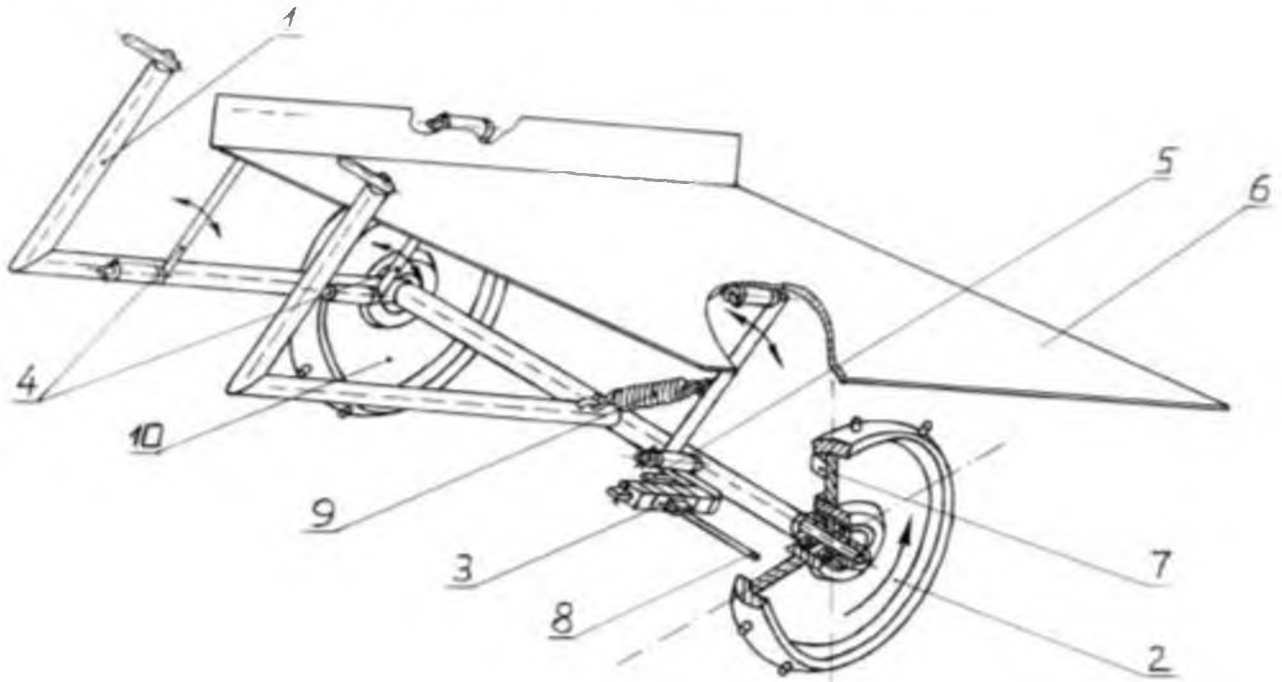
Схема удосконаленого розстиляльного пристрою стеблової стрічки льону: 1 – рама; 2 – опорно-приводне колесо; 3 – коромисло; 4 – підвіски; 5 – обмежувач ходу; 6 – вібрувальний щит ; 7 – язичок; 8 – палець; 9 – пружина; 10 – опорне колесо
